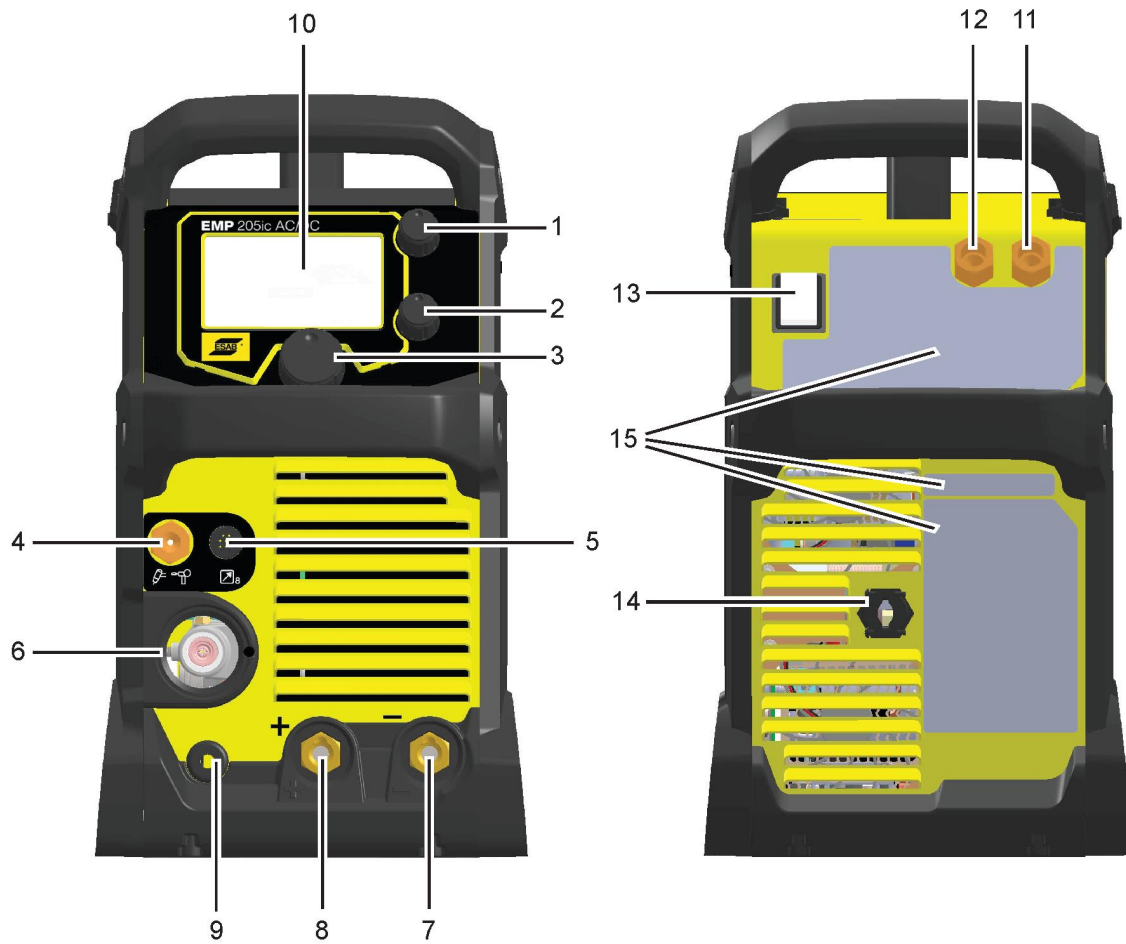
Vues avant et arrière : Modèle EMP 205ic c.a./c.c.
